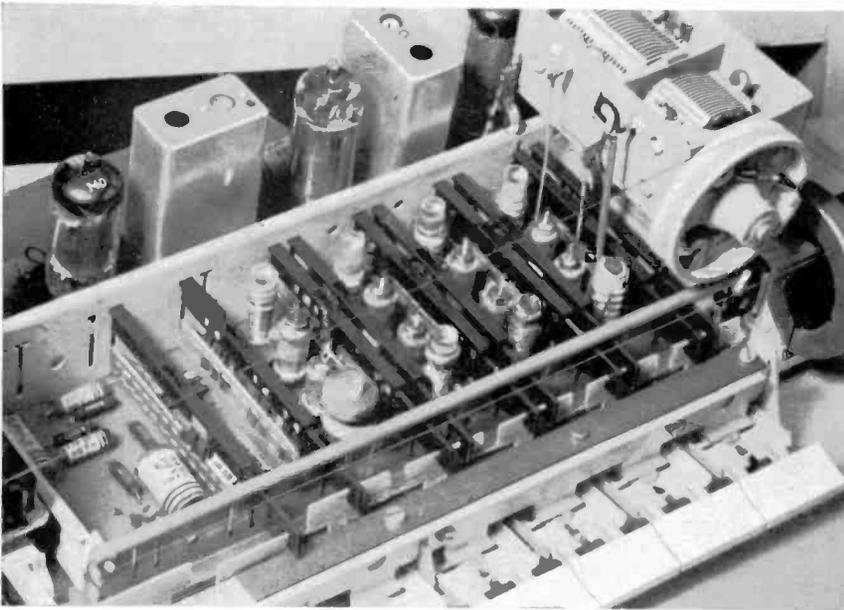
Drucktastenbestückung bei einer Exportausführung des 1098
